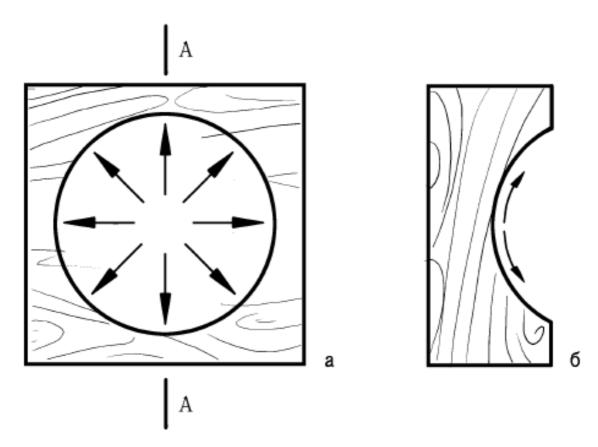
Выполнение круглой вогнутой выемки на торце заготовки вторым способом (стрелками показано направление движения инструмента): a – вид сверху;  $\delta$  – вид сбоку
